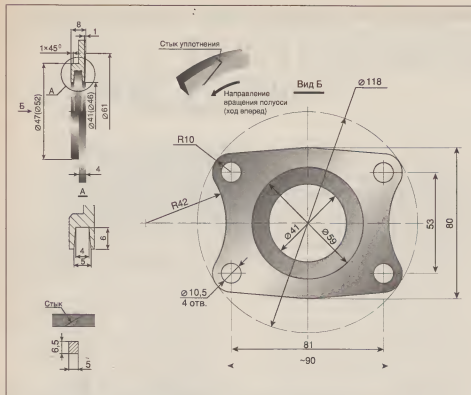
Крышка под подшипник от "Жигулей" (в скобках — для 207); профиль канавки и вайлочного кольца.
